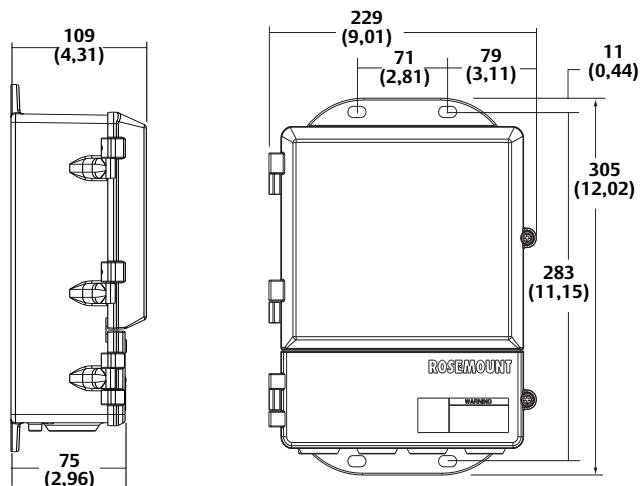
Габаритный чертеж преобразователя полевого монтажа
